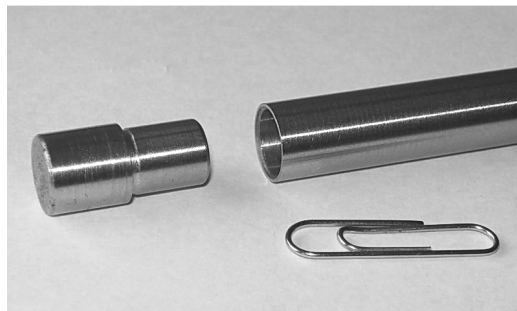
Фотография заглушки и трубки твэла до сварки
